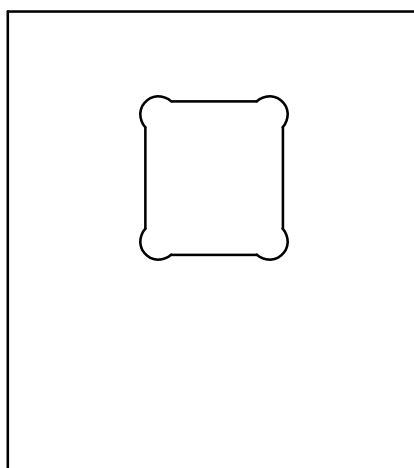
Adaptateur pour petites éprouvettes ayant les dimensions indiquées à la Figure 3 b)
